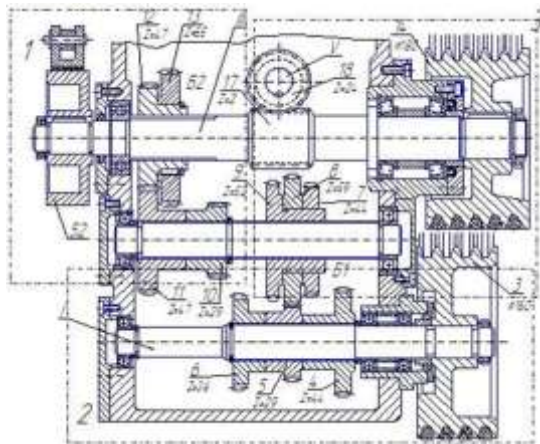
Коробка швидкостей зубообробного верстата
